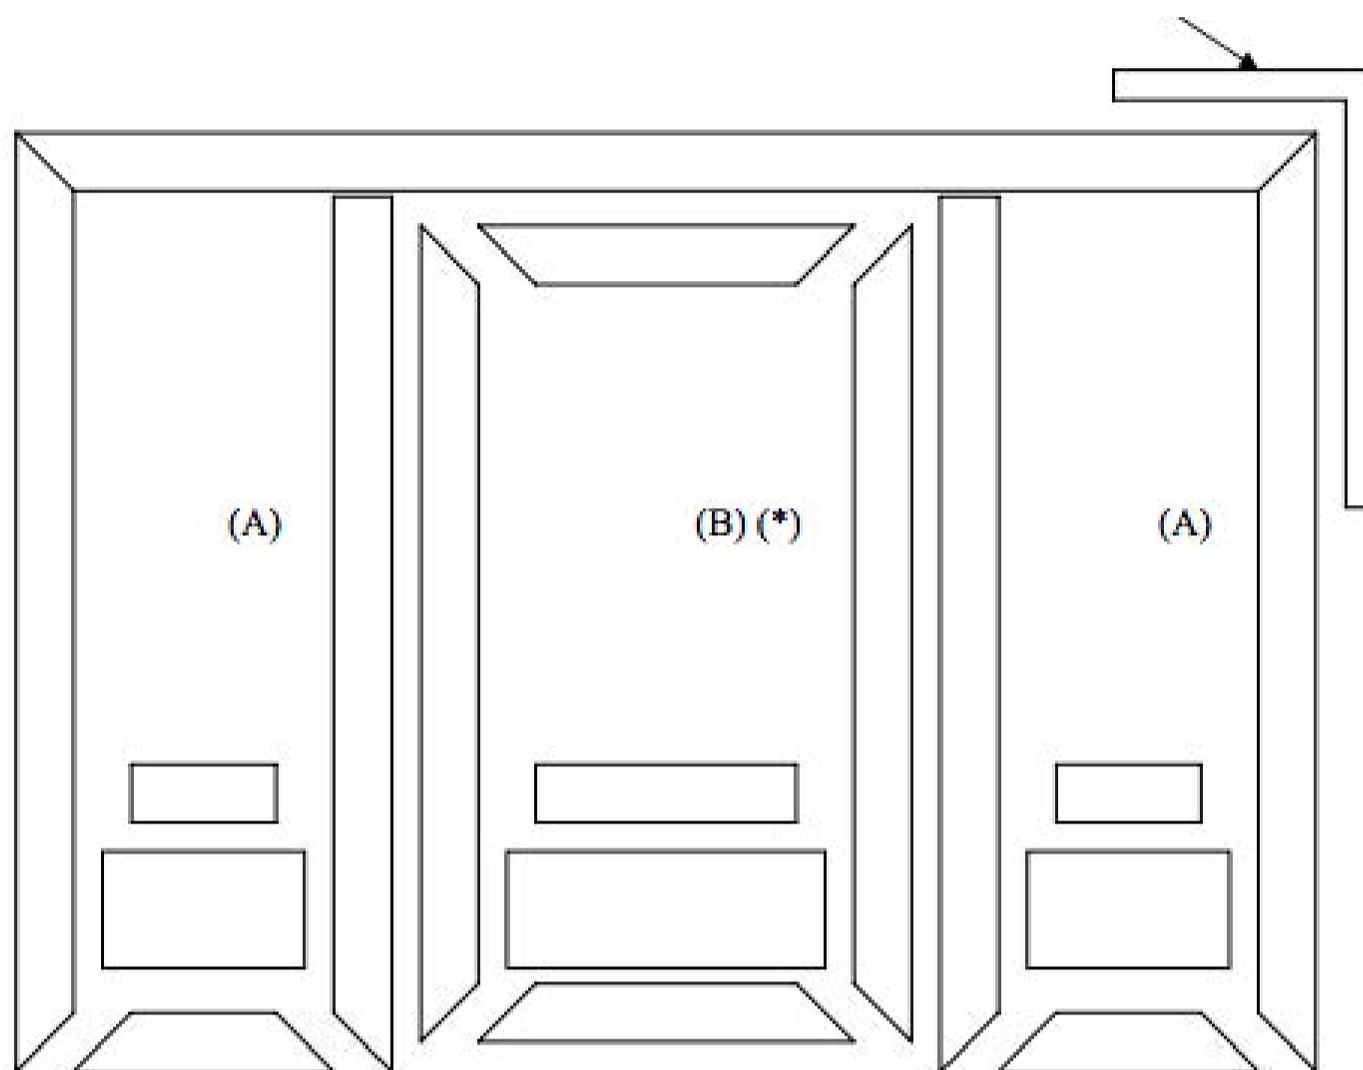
Después de colocarle los puntos de soldadura los paños fijos y la puerta, deben quedar como aparecen en la Fig. 8
